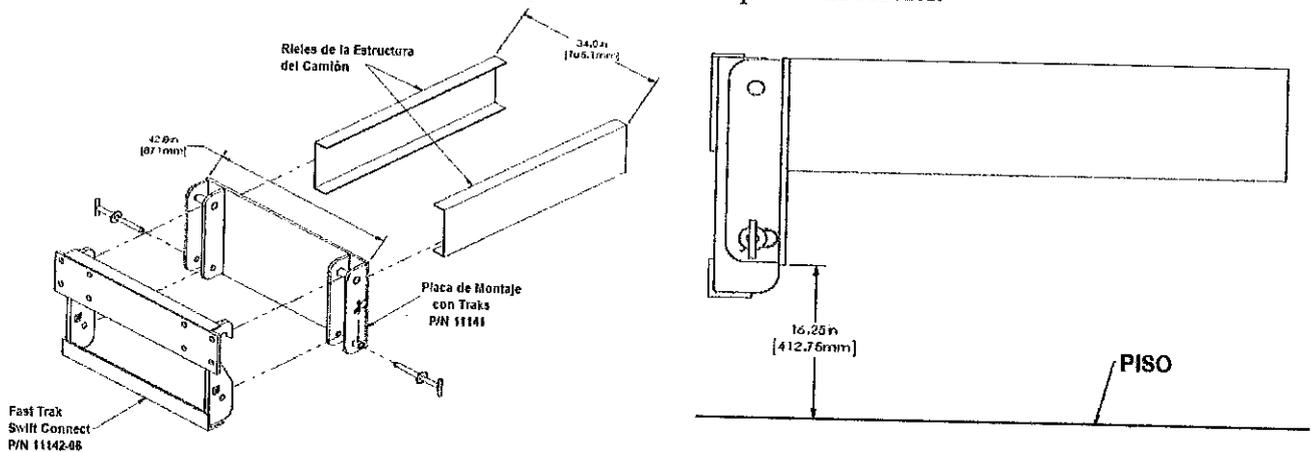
Vista a detalle y ensamblada de la Configuración 1.
